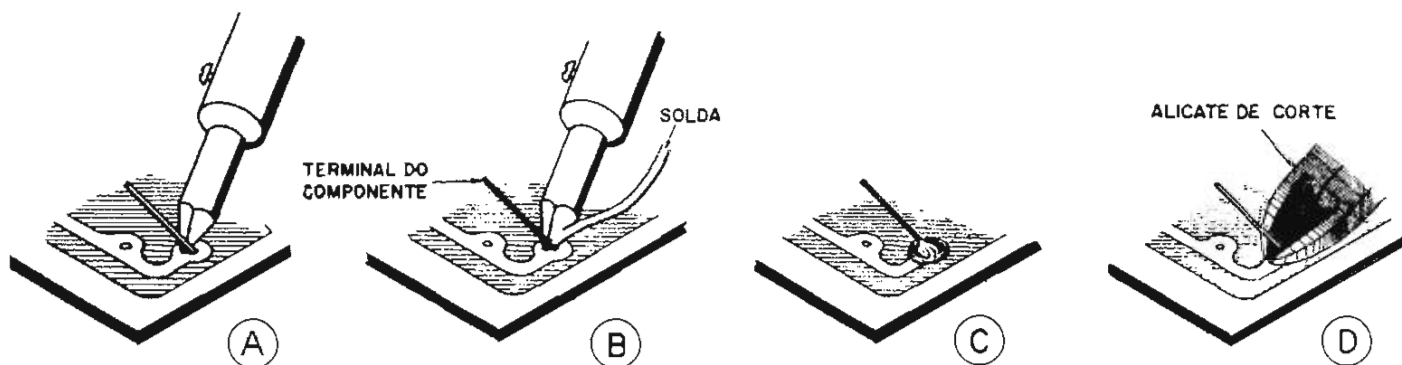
Diversas fases na soldagem de um componente à placa de tração impressa.
